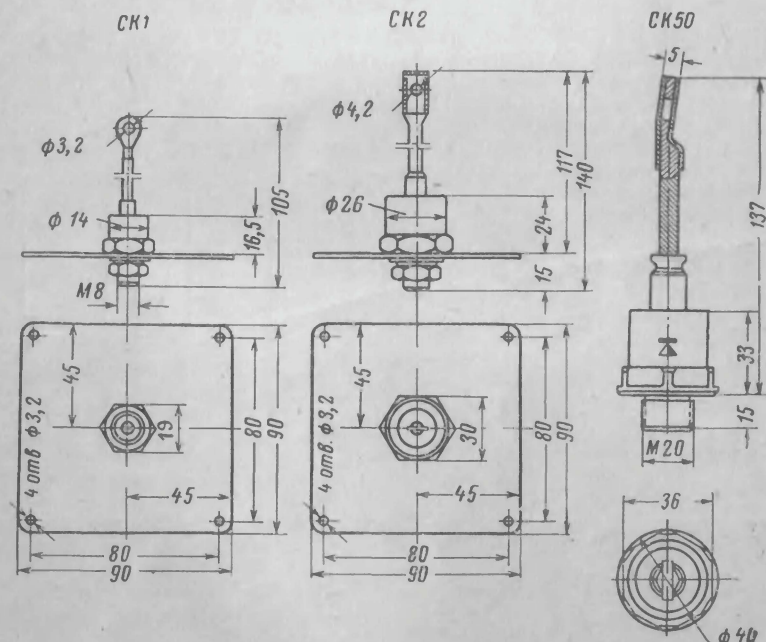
Габаритные чертежи мощных кремниевых стабилитронов и нормированные размеры радиаторов для стабилитронов СК1 и СК2.
